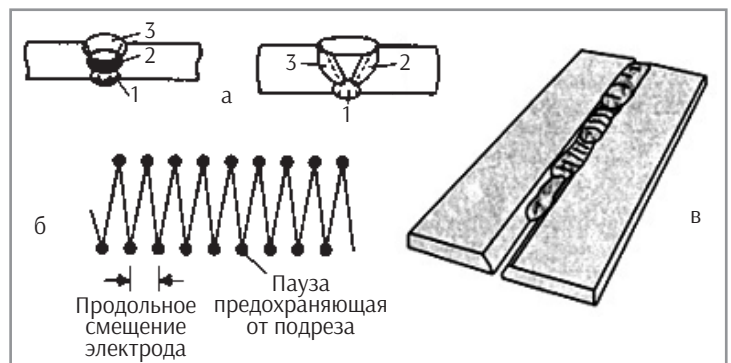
Сварка стыкового соединения со скосом кромок в нижнем положении: а — порядок наложения слоев; б — траектория движения электрода при выполнении последнего прохода; в — сварное соединение
